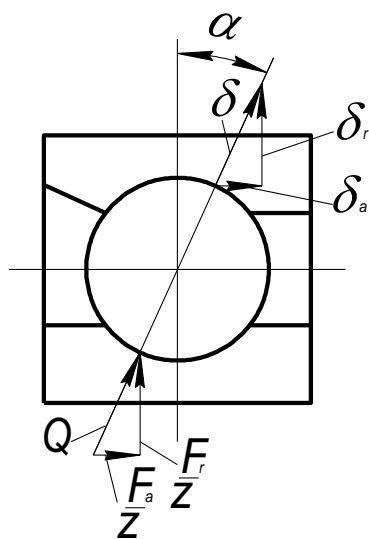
Схема нагружения шарика радиально-упорного подшипника силой натяга F_H
